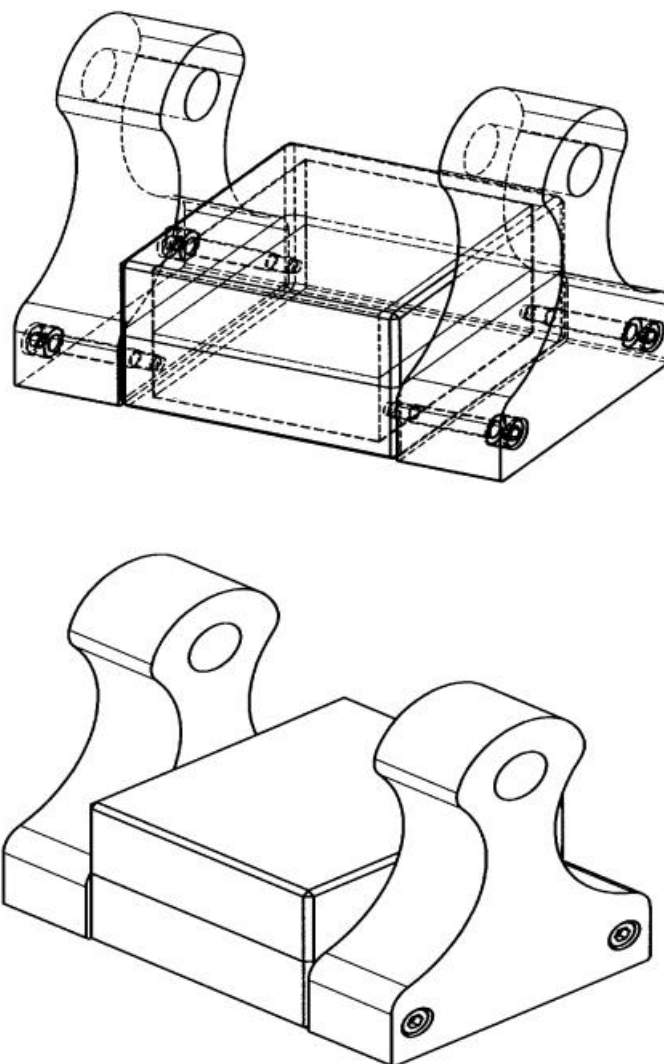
Gesamtansicht des Probenahmeschlittens.
